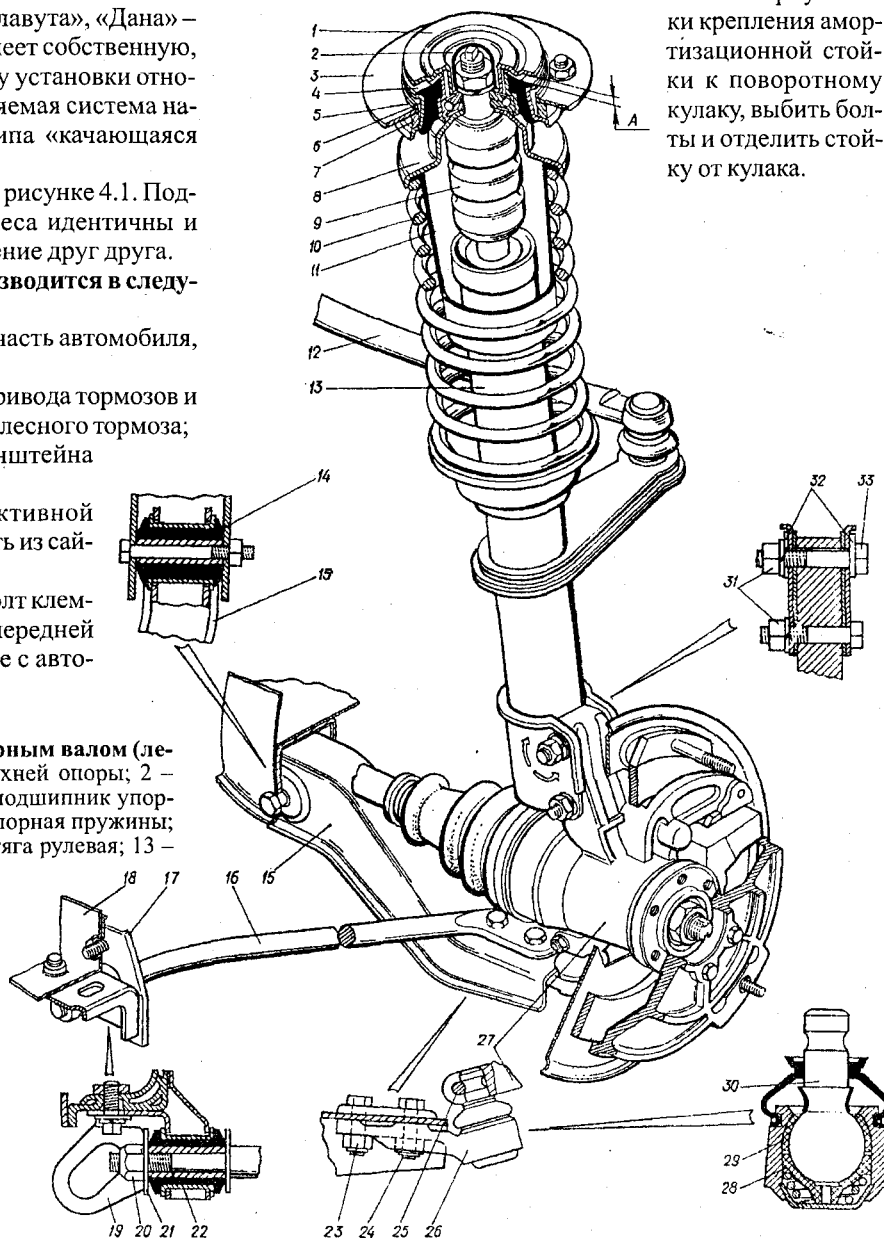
Передняя подвеска с шарнирным валом (левая сторона): 1 – ограничитель хода верхней опоры; 2 – колпачок; 3 – чашка кузова; 4 – гайка; 5 – подшипник упорный; 6 – опора; 7 – прокладка; 8 – чашка опорная пружины; 9 – буфер; 10 – пружина; 11 – чехол; 12 – тяга рулевая; 13 – амортизационная стойка; 14 – сайлентблок рычага; 15 – рычаг; 16 – штанга реактивная; 17 – кронштейн; 18 – поперечина кузова; 19 – буксирная проушина; 20 – гайка крепления реактивной штанги; 21 – шайба; 22 – сайлентблок; 23 – гайка крепления нижнего шарнира; 24 – болт; 25 – стяжной болт клеммового соединения; 26 – шарнир нижний; 27 – поворотный кулак; 28, 29 – вкладыши нижний и верхний; 30 – палец шаровой; 31 – гайки крепления амортизационной стойки к поворотному кулаку; 32 – шайбы специальные; 33 – болт специальный; А – при технически исправных деталях подвески зазор (в продольной оси автомобиля) должен быть не более 10 мм
